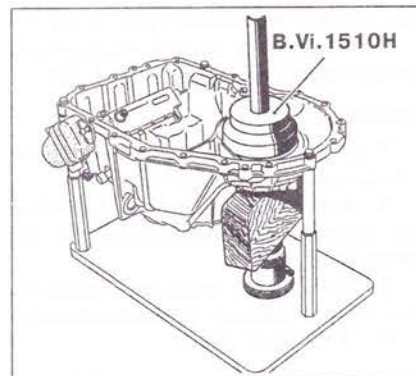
Установите опору подшипника дифференциала при помощи приспособления В. Ви. 1510Н.
